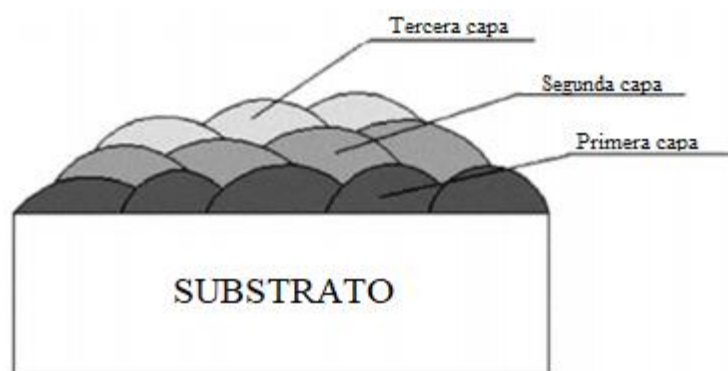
Esquema de capas de soldadura em hardfacing – 5 mm de espesor por capa
